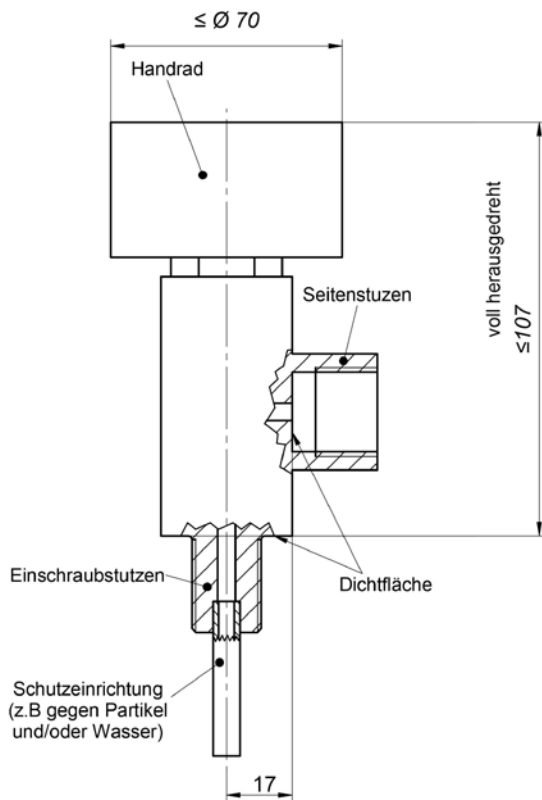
Druckgasbehälterventil Typ 1 (alle Maße in mm)
